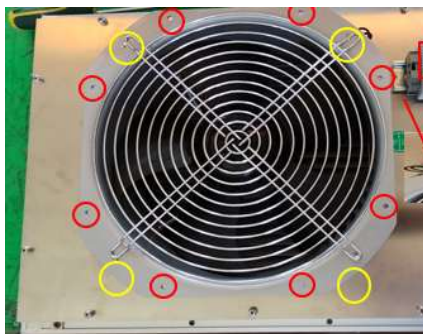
Orifícios de fixação do ventilador de dissipação de calor e orifícios de fixação do filtro do ventilador
